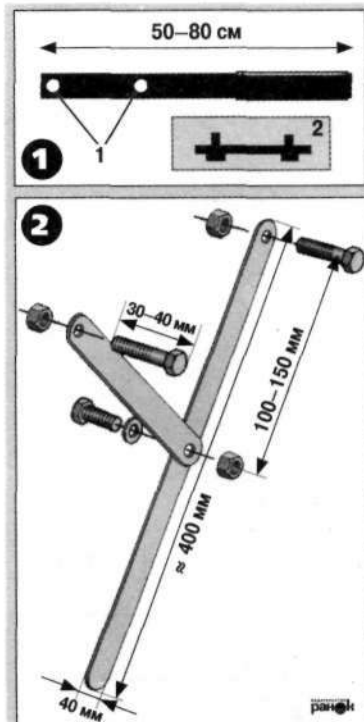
Приспособления для фиксации корпуса автоматического сцепления.
